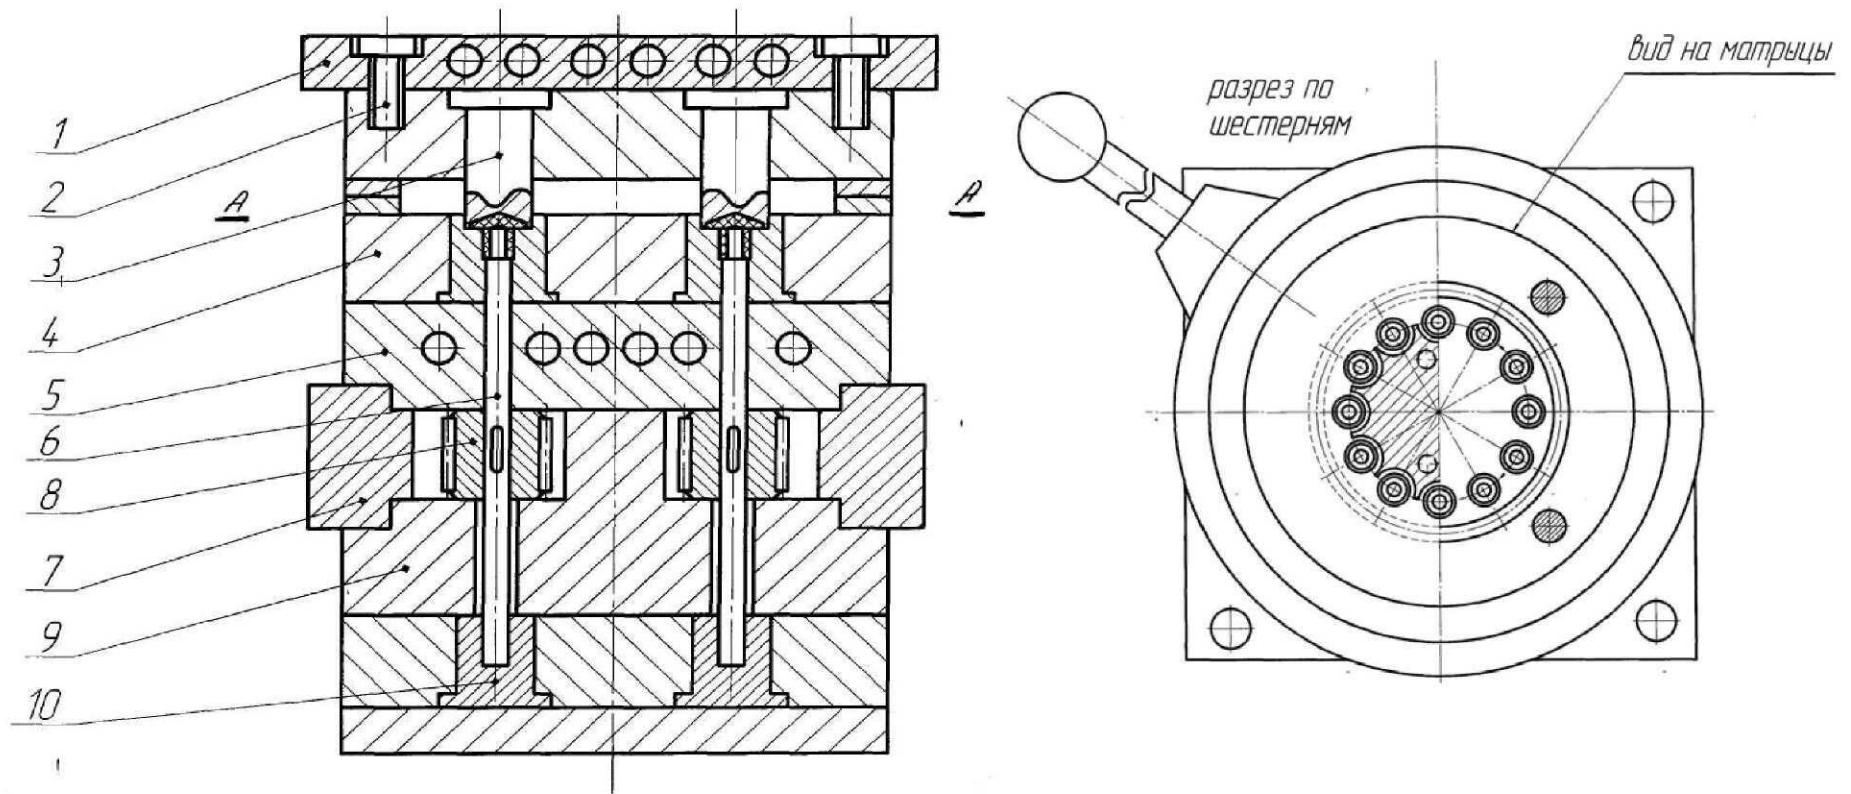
Пресс-форма для изготовления изделий методом прессования:
